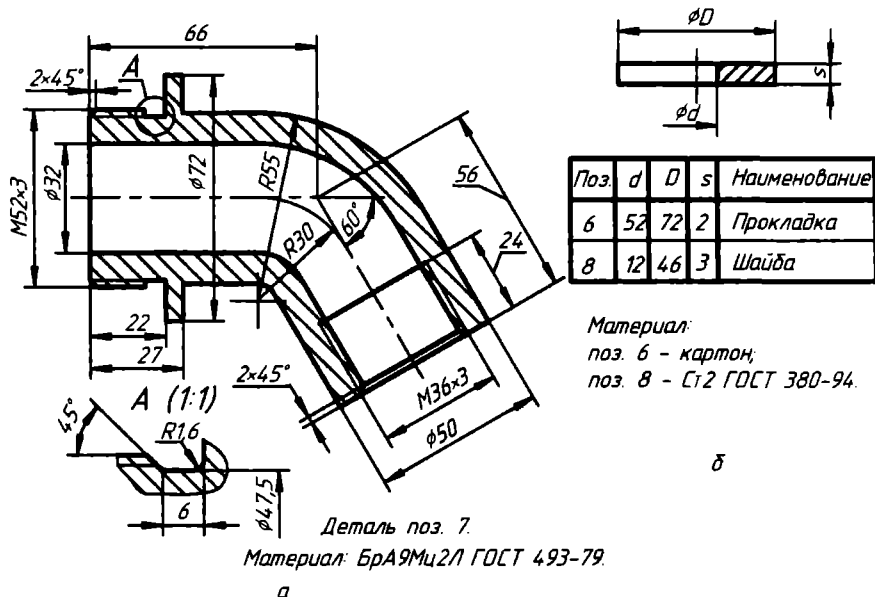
Чертежи: а — колена; б — прокладки, шайбы
